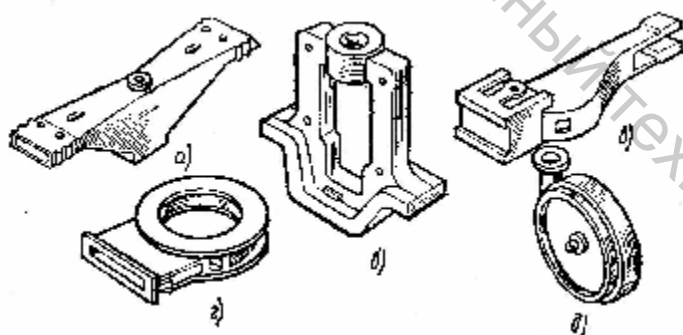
Отливки четвертой группы сложности: а- шкворневая балка ; б- станина станка; в- ползун; г- корпус шибера; д- улитка
